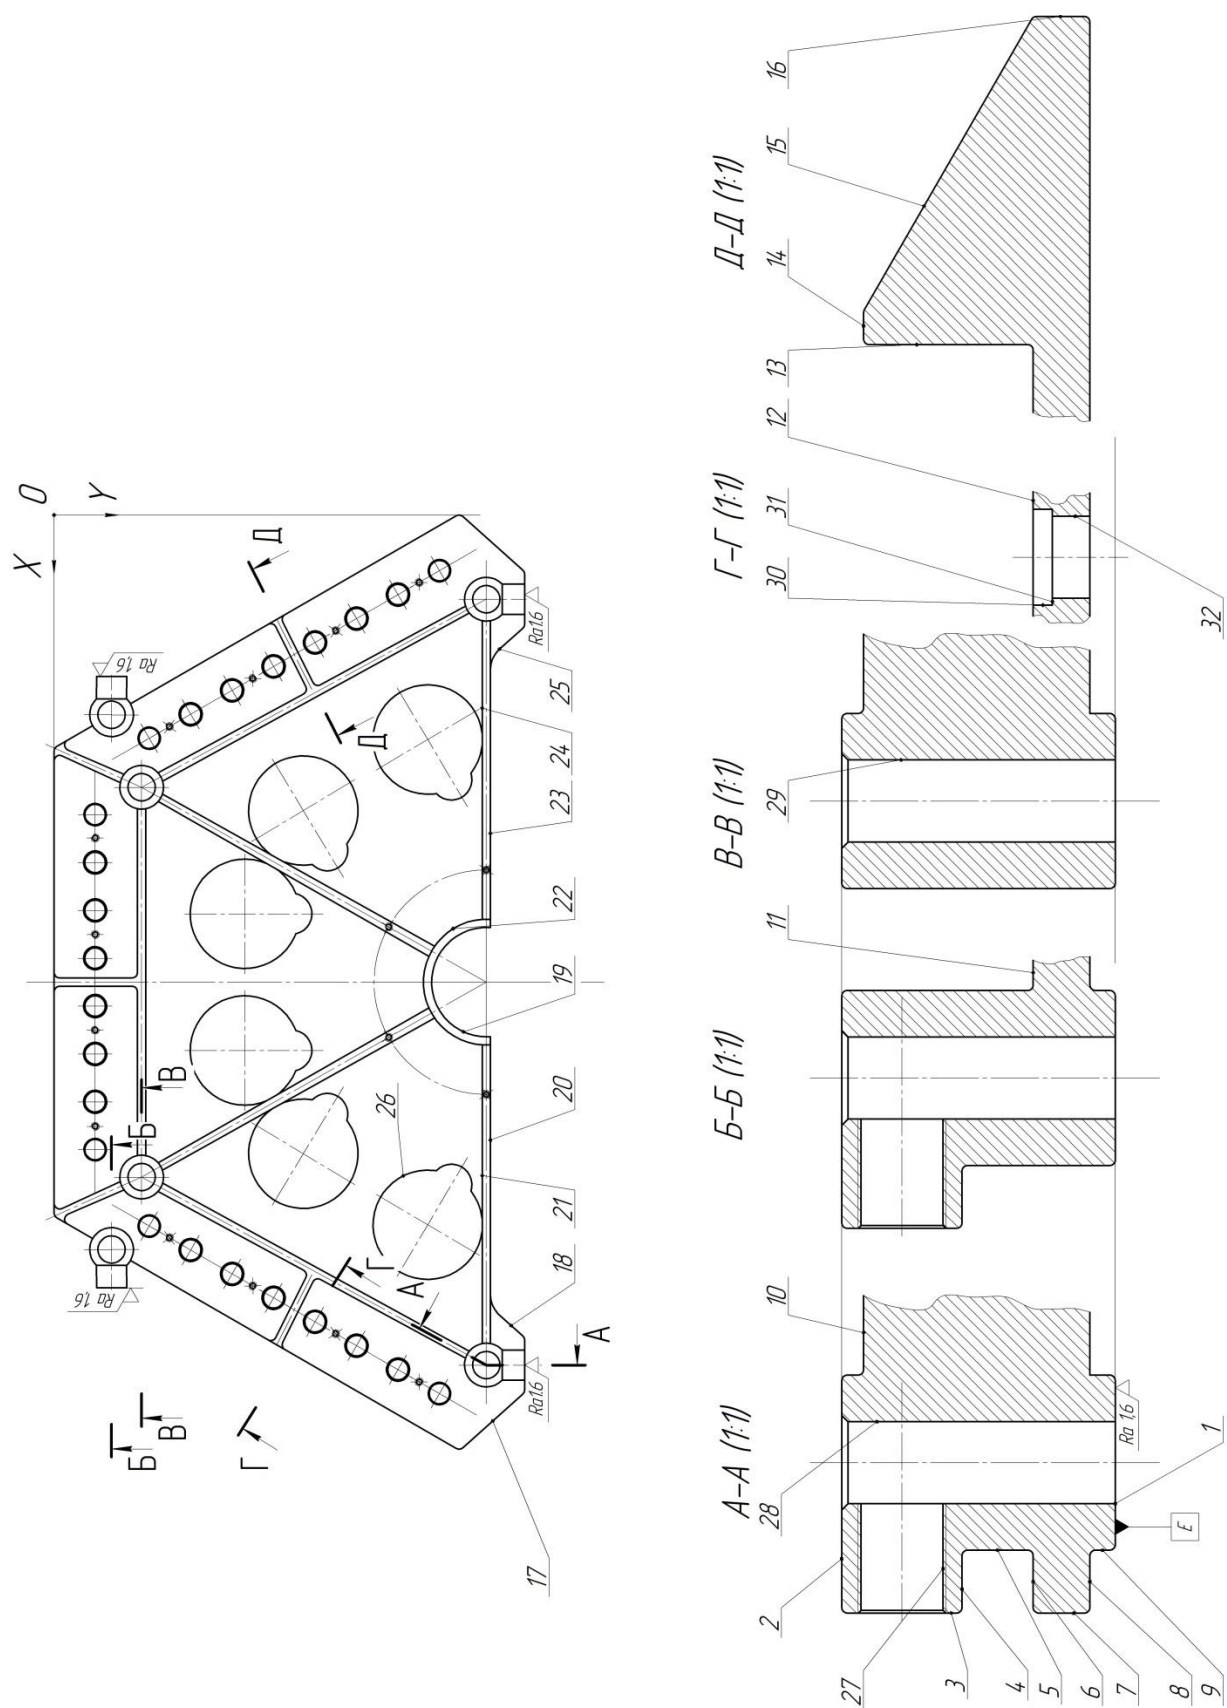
Деталь - «Корпус плиты кондуктора», общий вид
